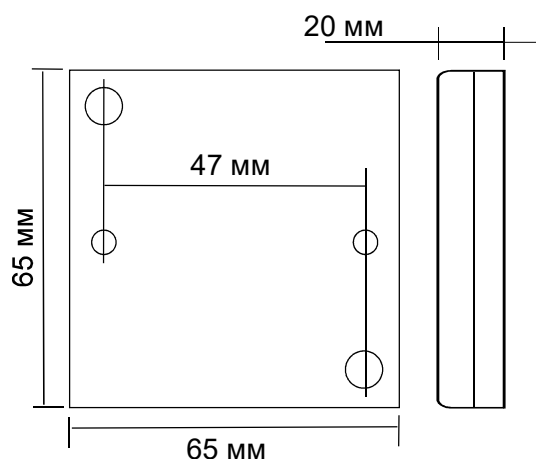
Габаритные размеры корпуса контроллера Рис.2 Внешний вид платы контроллера
